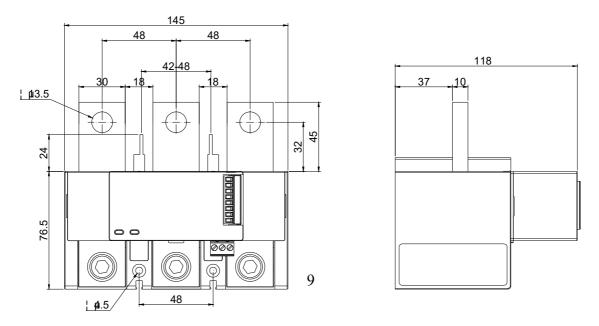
Внешний вид и габаритные размеры КСМ-М4-400
